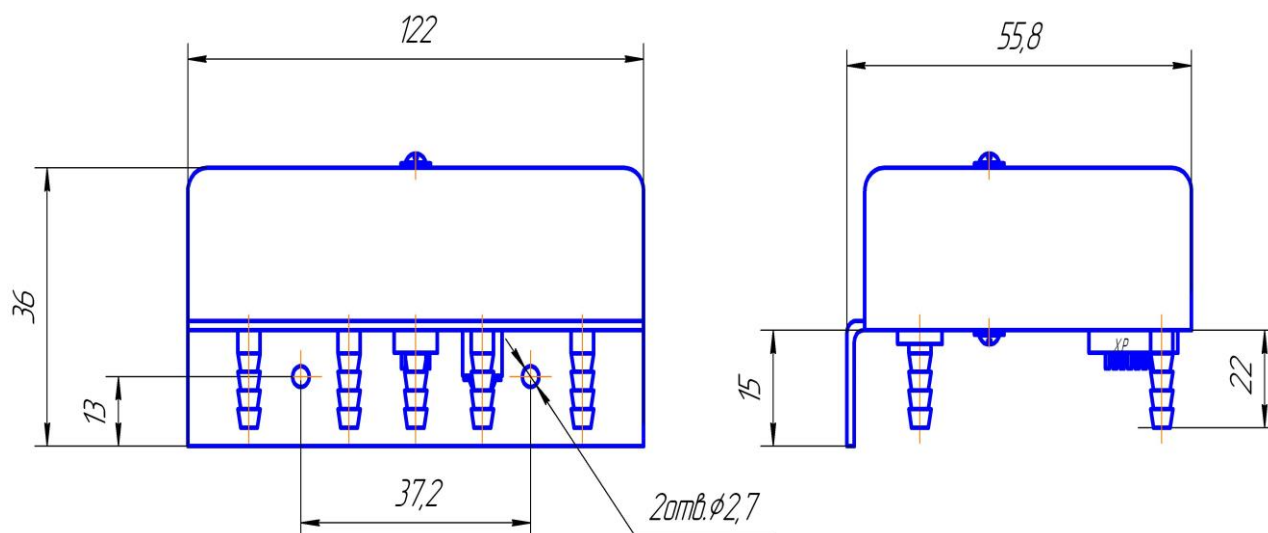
б - Габаритные и присоединительные размеры устройства УПС-04
